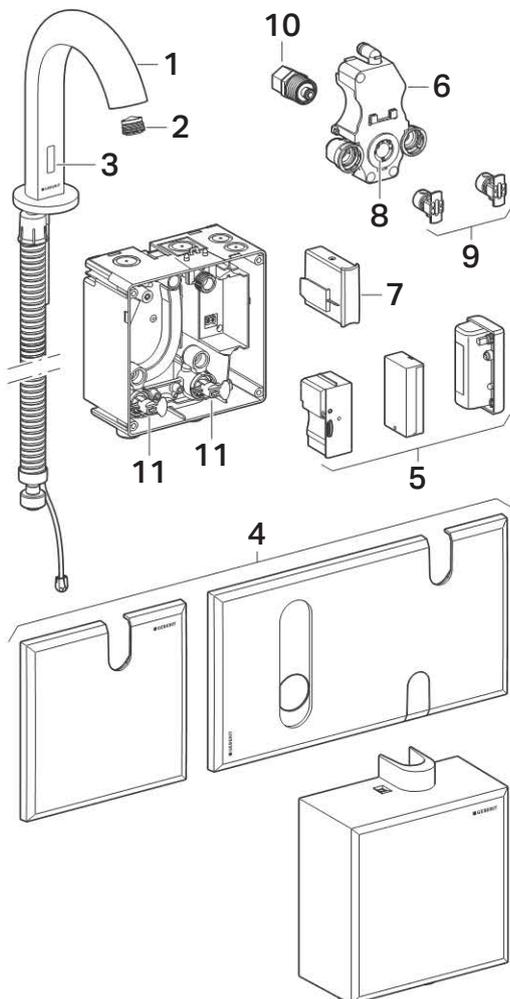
Rubinetterie per lavabo Geberit Piave e Brenta, montaggio a pianale
